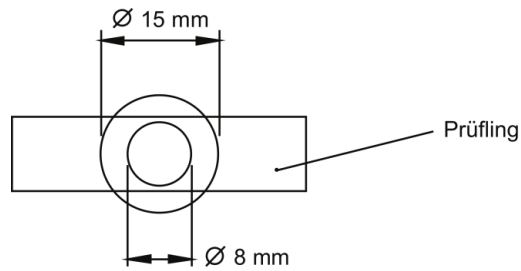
Vorrichtung für die Kugeldruckprüfung gemäß 25.2 und 25.3
